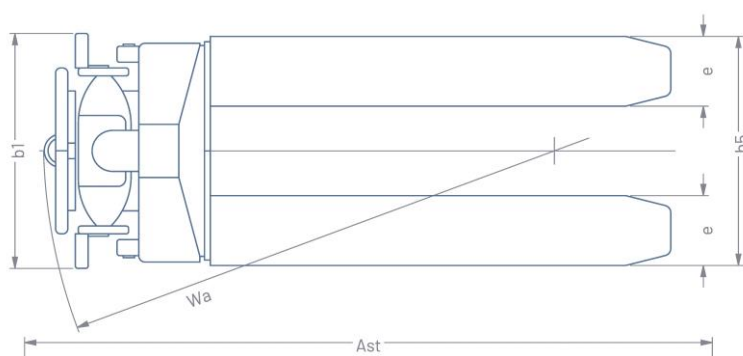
ZAC-C Draufsicht mit Kürzeln
